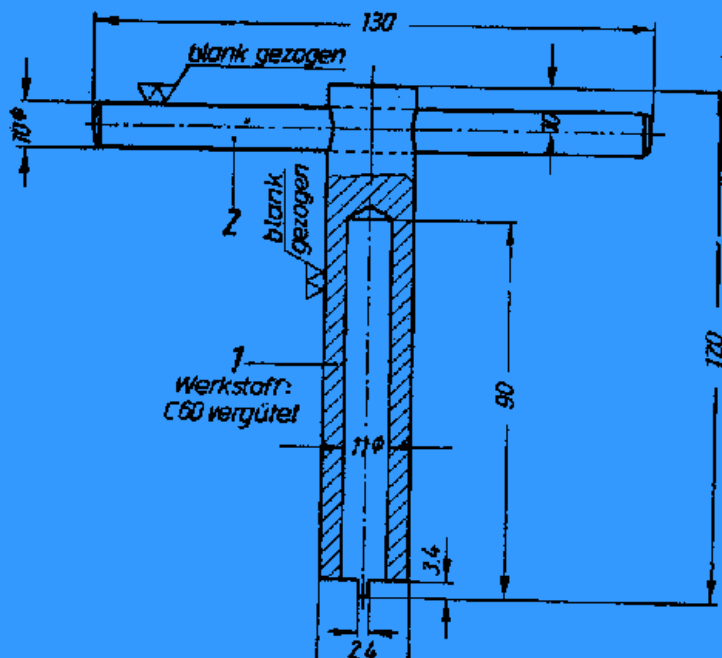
Steckschlüssel für die Schlitzmutter im Gabelfuß
